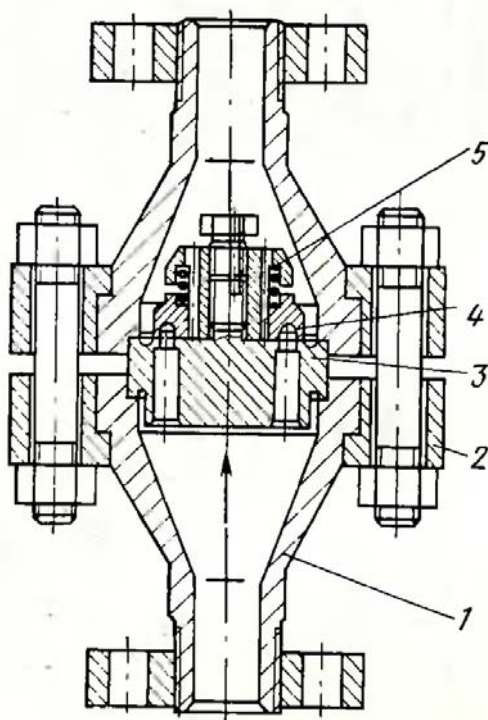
Обратный подъемный тарельчатый фланцевый типа 16с30нж
